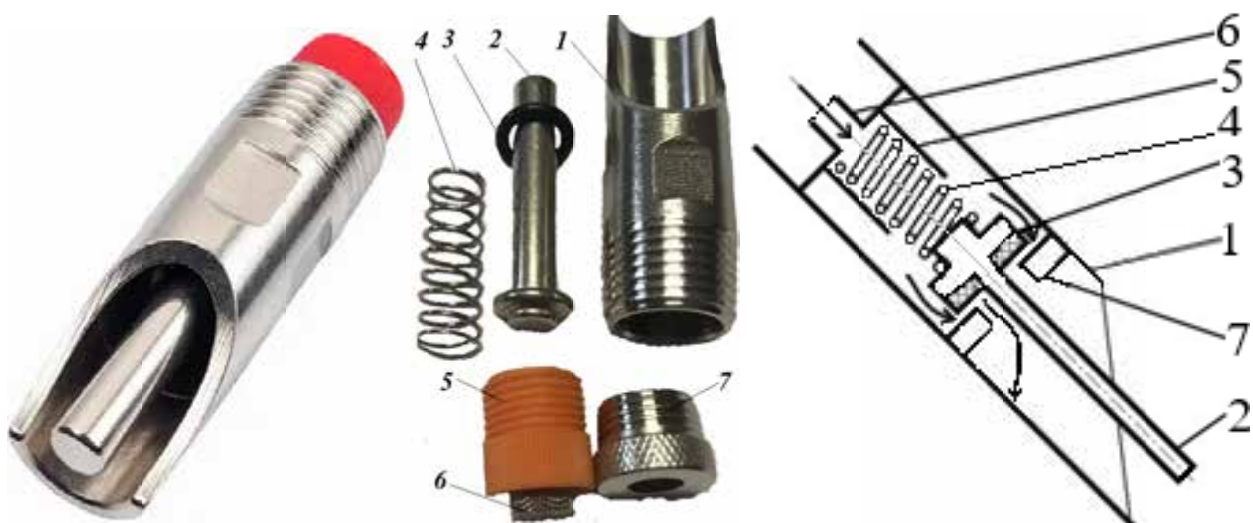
Конструкційна схема соскової напувалки з пружинним механізмом:
